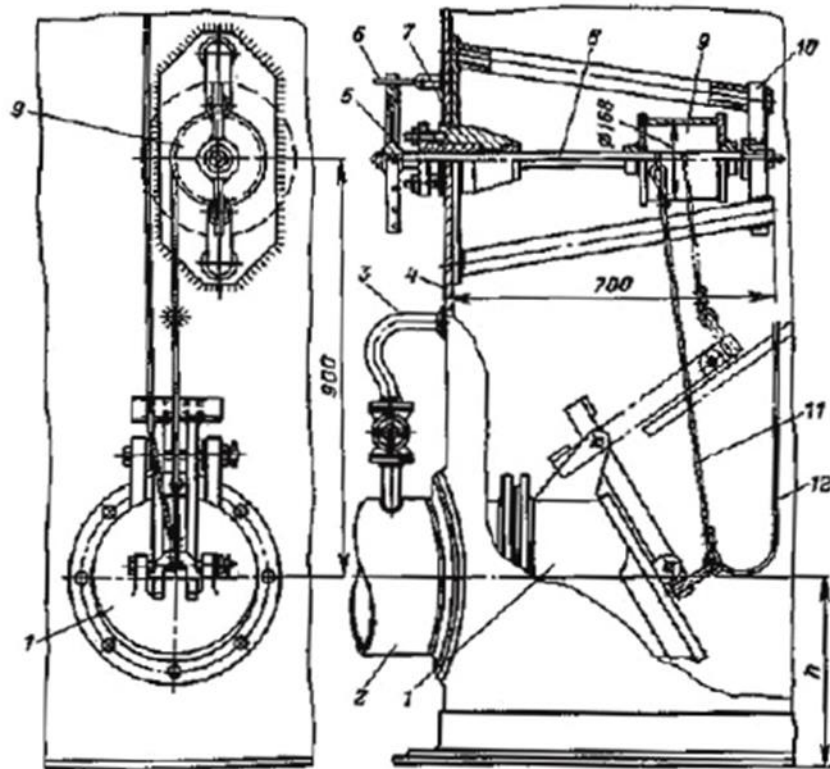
Механізм бокового управління хлопавкою РВС: 1 – хлопавка; 2 – приймально-роздаточний патрубок; 3 – перепускна труба с вентилем; 4 – стінка резервуару; 5 – штурвал; 6 – стопор; 7 – сальник; 8 – вал; 9 – барабан; 10 – кронштейн; 11 – трос; 12 – запасний трос
